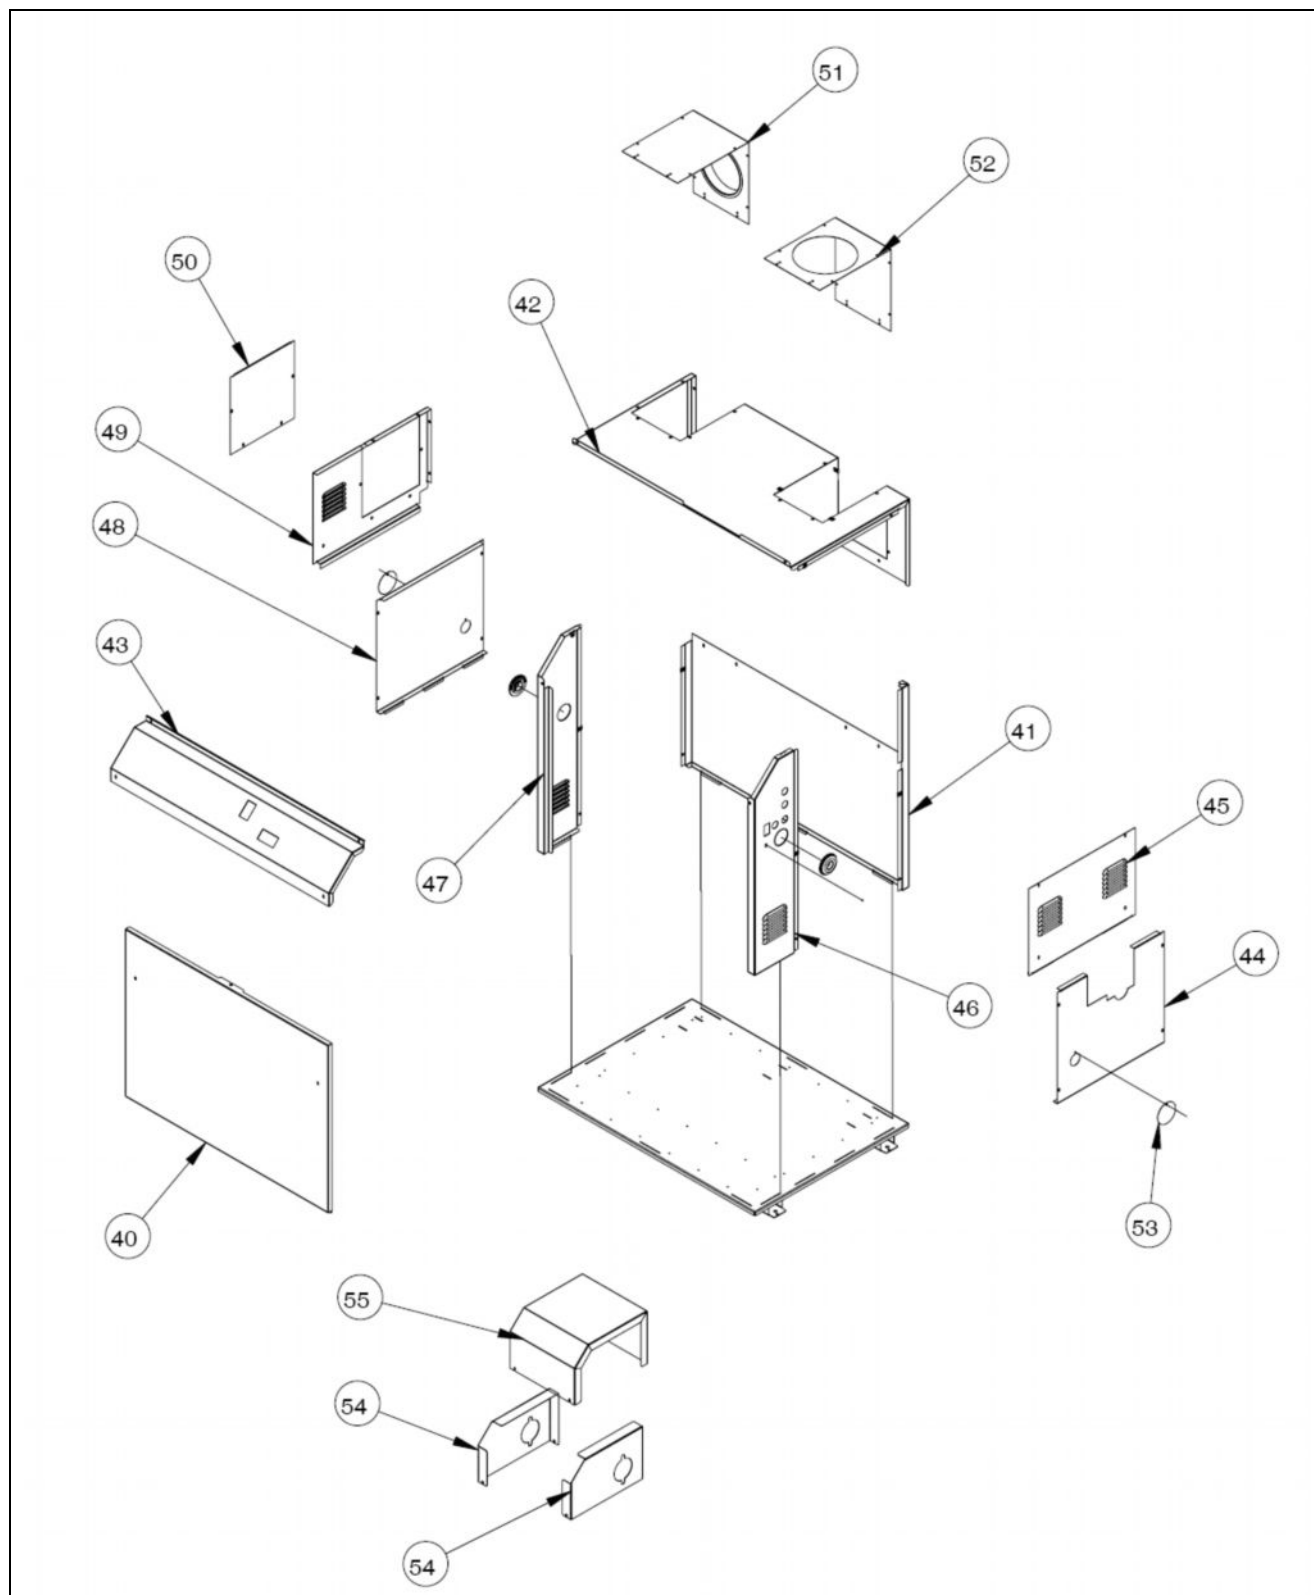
Детали корпуса котла Пеннант, типоразмеры 200 – 400.
